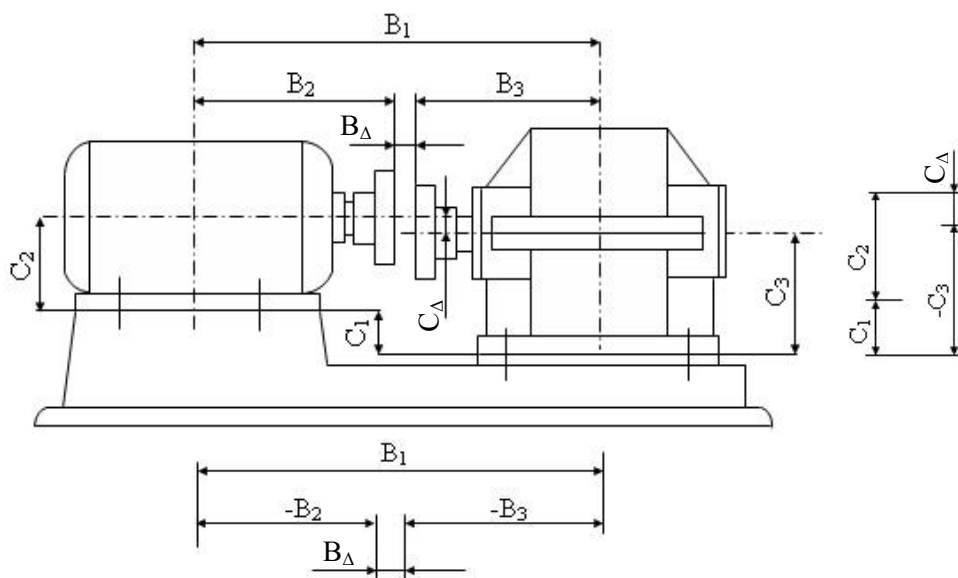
Сборочная единица "двигатель-редуктор" и схемы размерных цепей по монтажным размерам
